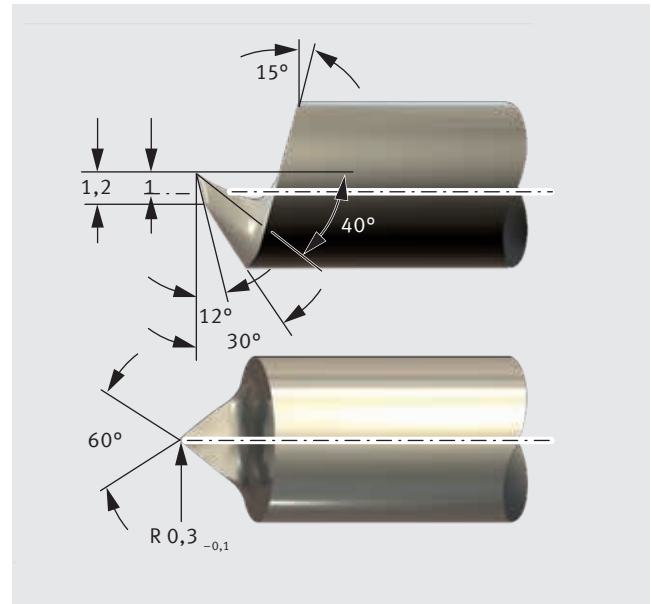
Schneidwerkzeug für KS Permaglide® P22 und P202
